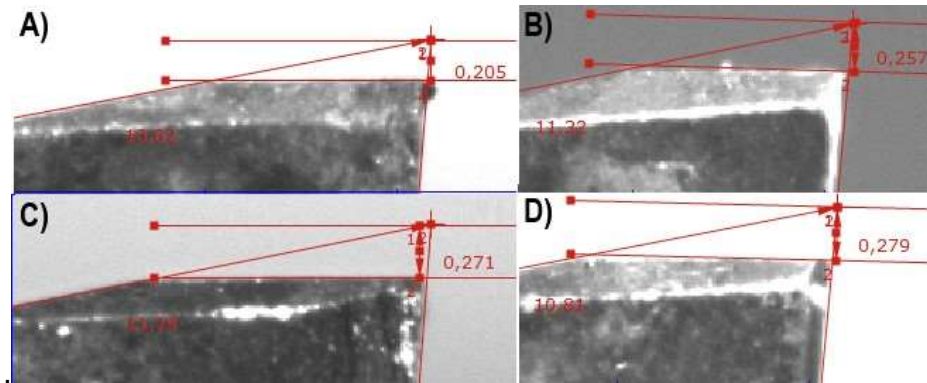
Desgaste del flanco VB de insertos sin recubrir N5, condiciones de corte: A) 20, B) 30, C) 40 y D) 60m/min.
